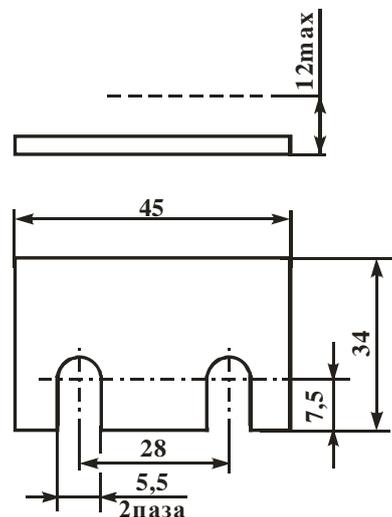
Габаритные и присоединительные размеры Э31-В9
